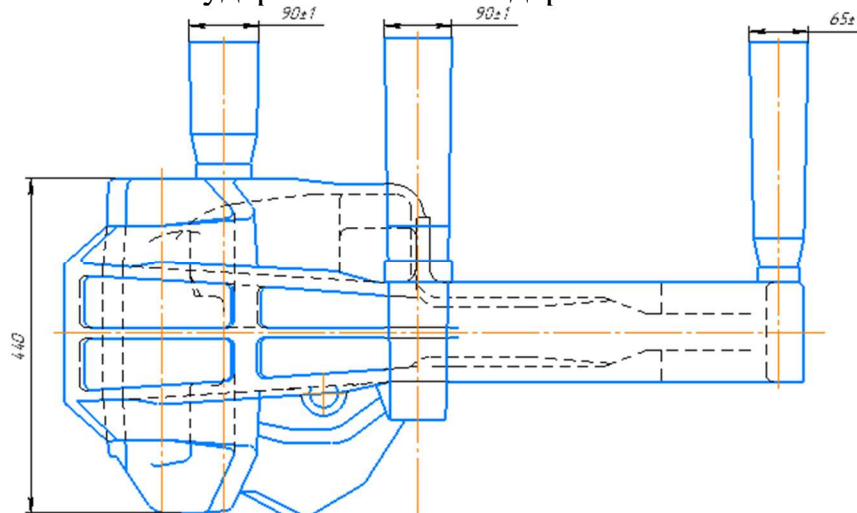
Фрагмент чертежа «Отливка корпуса автосцепки СА-3 с литниковыми элементами»
